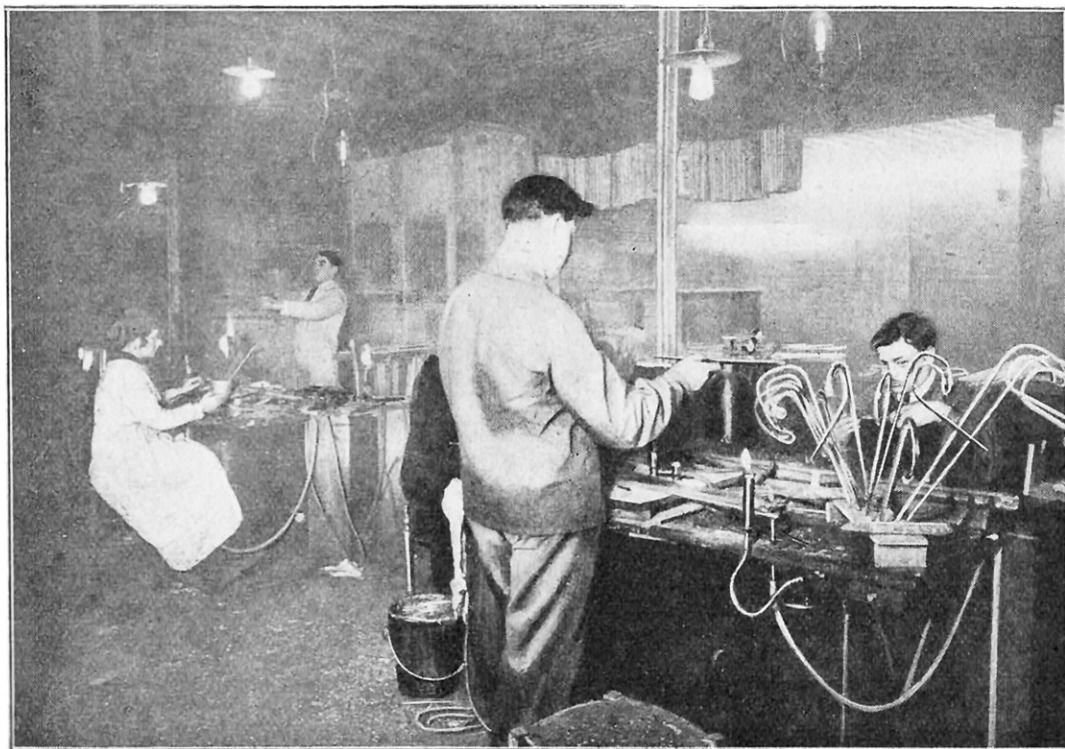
ATELIER DE CONFECTION DES PETITS TUBES QUI SERONT ASSEMBLÉS POUR CONSTITUER DES ENSEIGNES OU DES DÉCORS LUMINEUX QUELCONQUES
